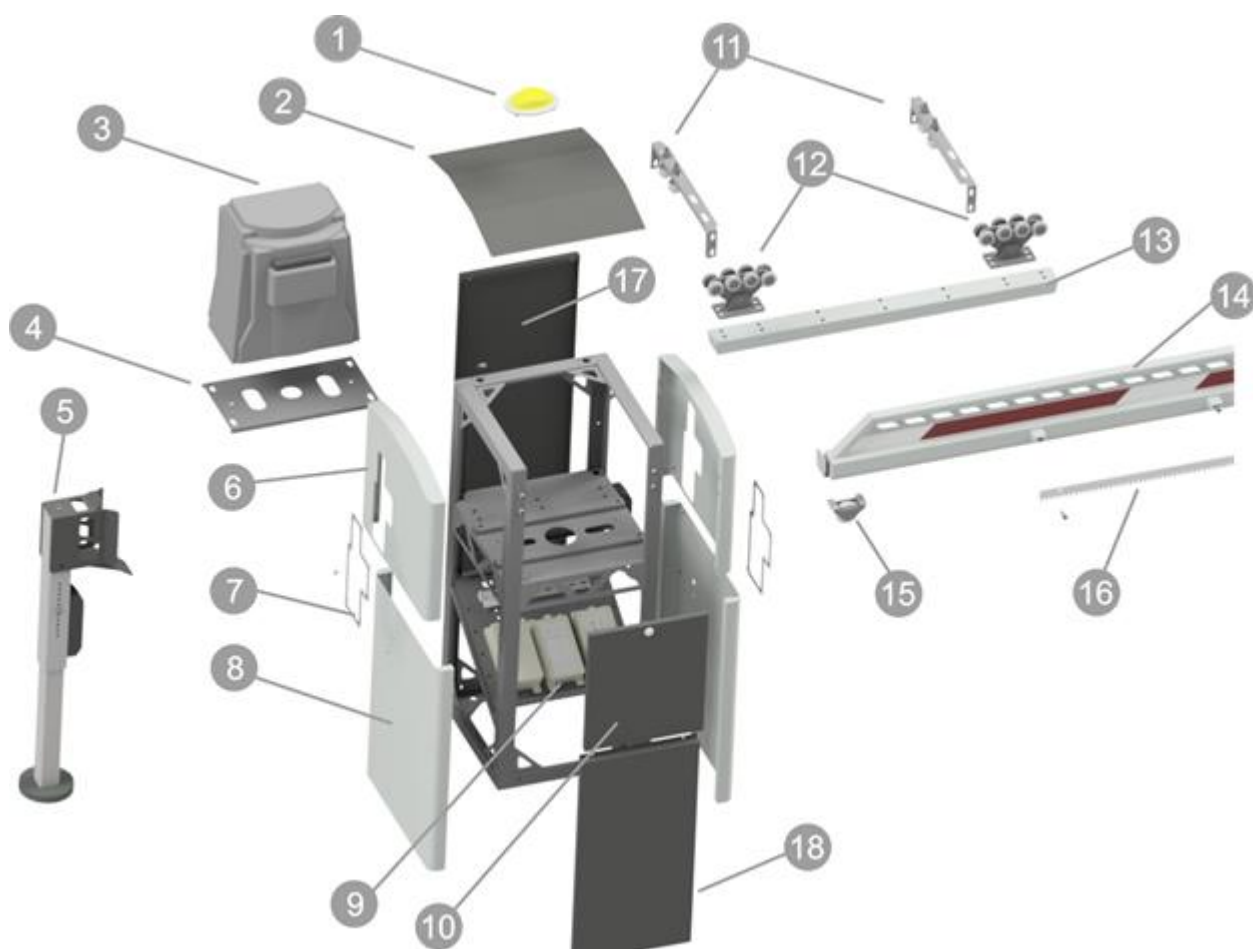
Устройство шлагбаума ЛКД-ТШО.
